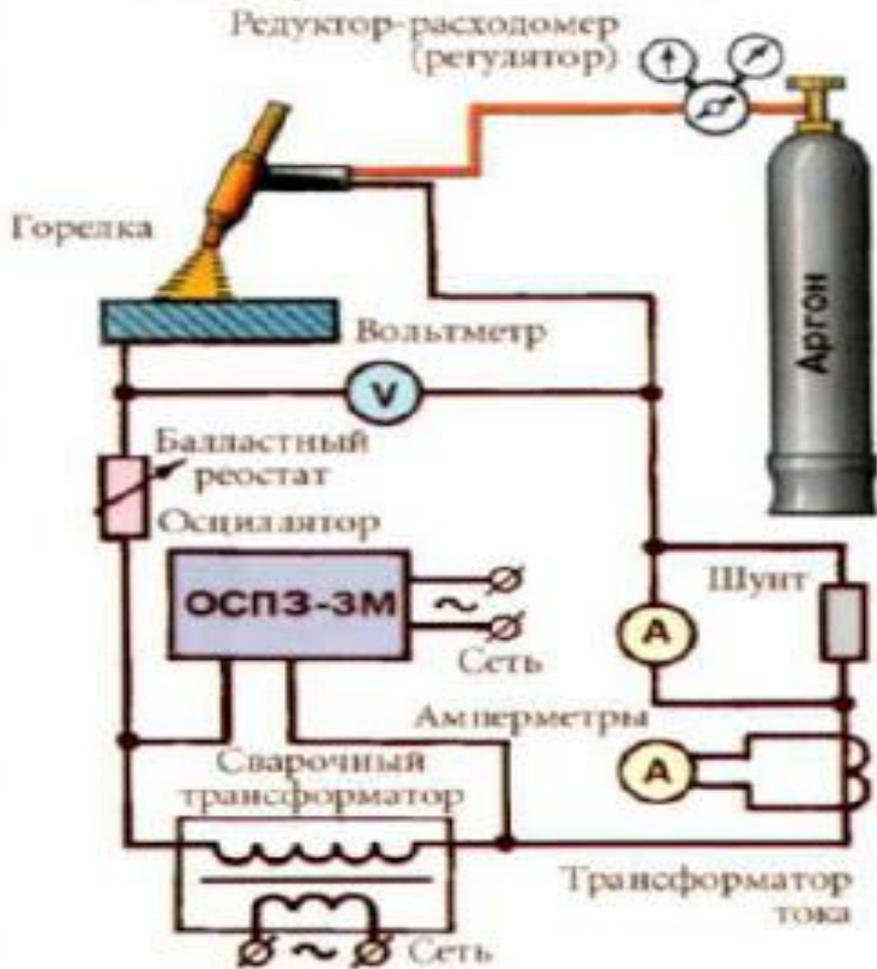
Схема поста аргонодуговой сварки неплавящимся электродом:
